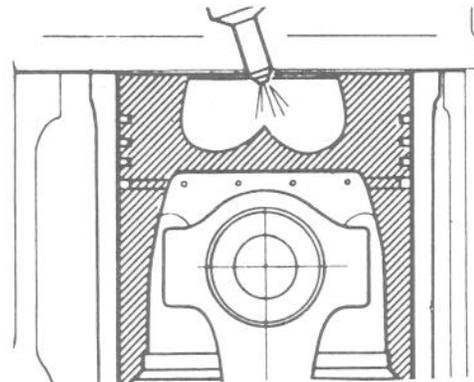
Cámara de combustión para un motor de inyección directa.
